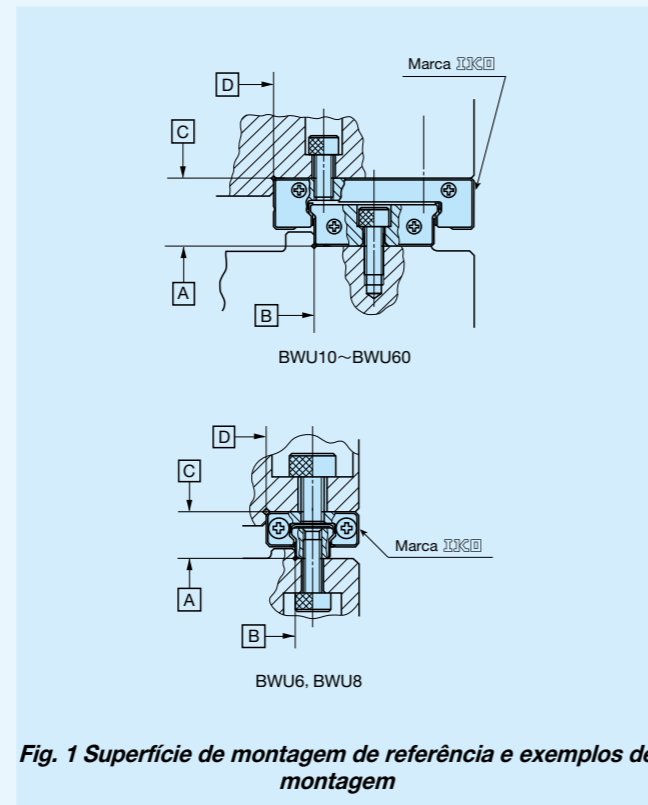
Superfície de montagem de referência e exemplos de montagem
